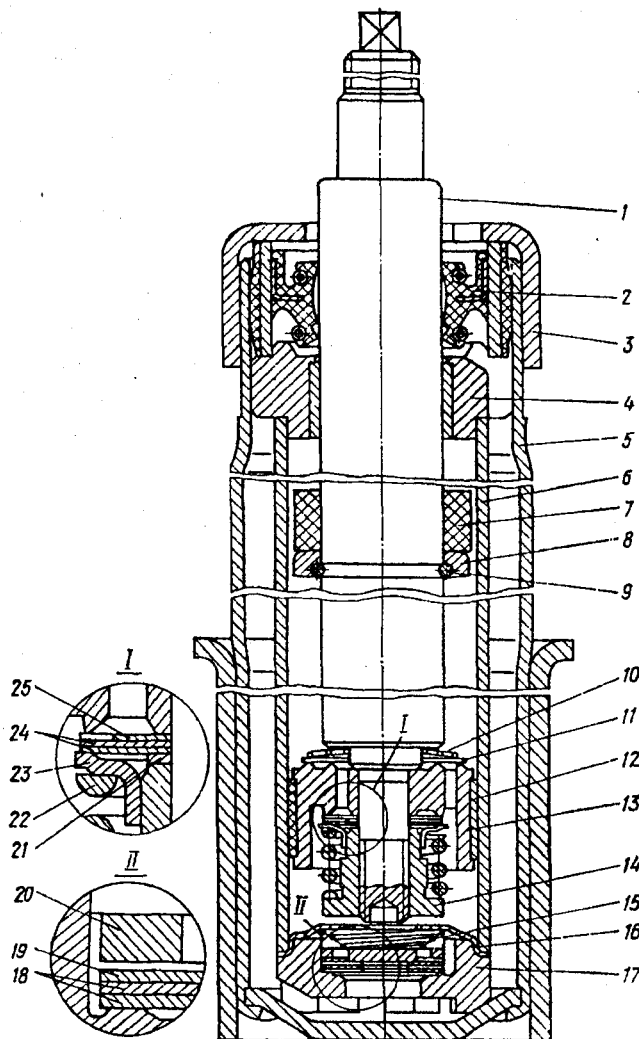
Амортизатор стойки передней подвески: 1 - шток; 2 - сальник; 3 - гайка резервуара; 4 - втулка направляющая; 5 - резервуар; 6 - цилиндр; 7 - буфер хода отдачи; 8 - тарелка ограничительная; 9 - кольцо ограничительное; 10 - пружина перепускного клапана; 11 - тарелка перепускного клапана; 12 - кольцо поршня; 13 - поршень; 14 - гайка клапана отдачи; 15 - пружина перепускного клапана; 16 - обойма клапана сжатия; 17 - корпус клапана сжатия; 18 - диск клапана сжатия; 19 - диск дроссельный клапана сжатия; 20 - тарелка; 21 - шайба гайки; 22 - пружина клапана отдачи; 23 - тарелка упорная; 24 - диск клапана отдачи; 25 - диск дроссельный клапана отдачи; I - клапан отдачи; II - клапан сжатия
